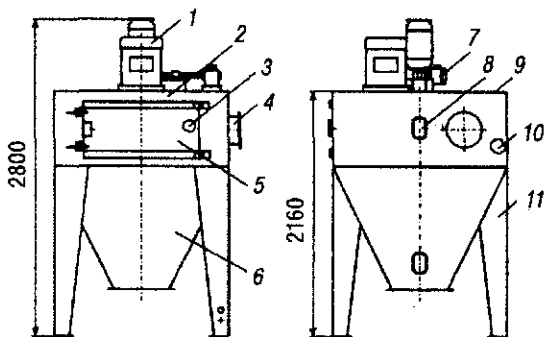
Схема молотковой дробилки типа Р1-БДК:
